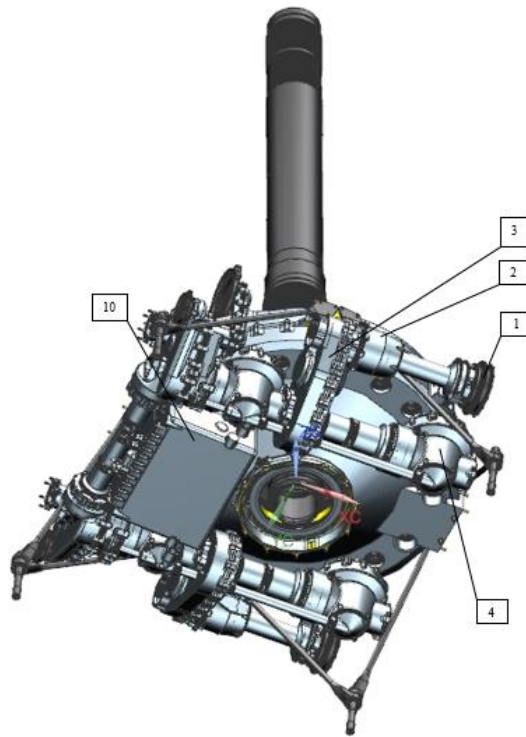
Главный редуктор ВР-450, вид снизу
